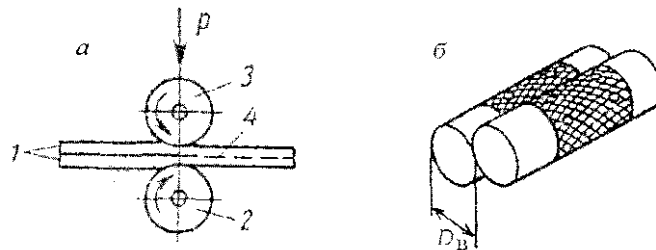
Схема контактно – теплового зварювання із застосуванням роликів (а) та валиків (б): 1 - матеріал, що зварюється; 2 - нагрітий ролик; 3 — притискний ролик; 4 — зварний шов.
